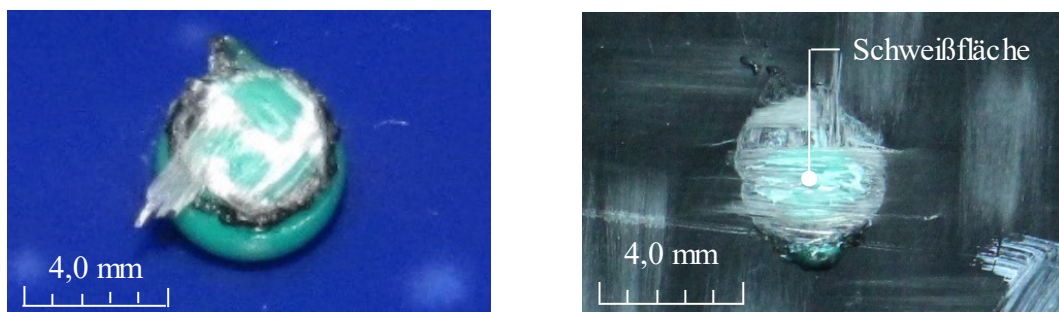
Sichtprüfung der Schweißverbindung PP-GF/PP nach dem Kopfzugversuch [138]
